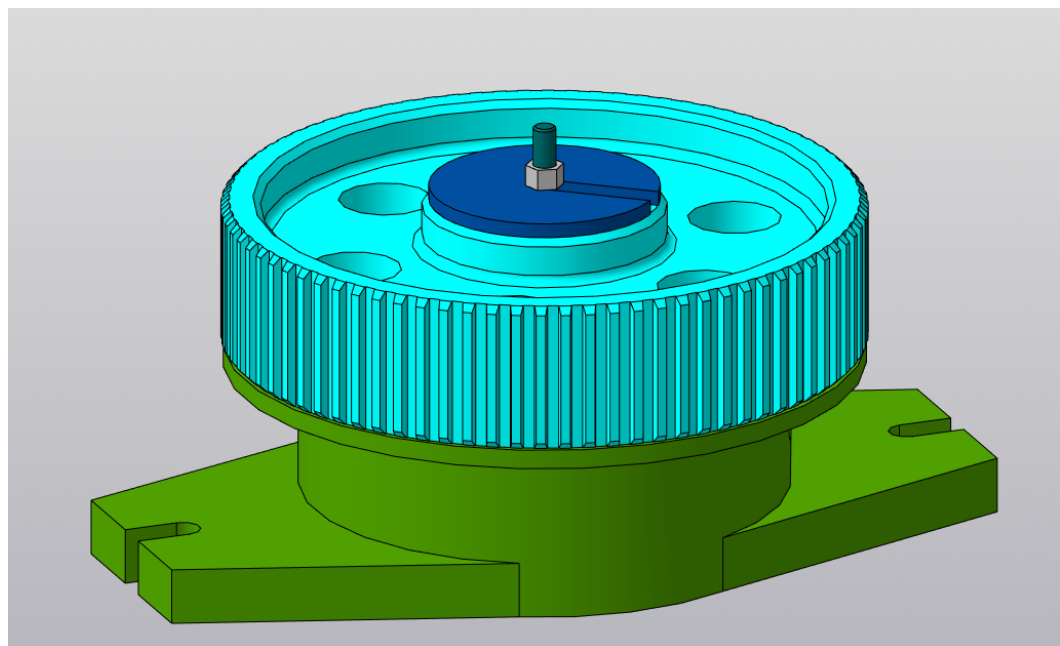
Спроектований верстатний пристрій та закріплена деталь
